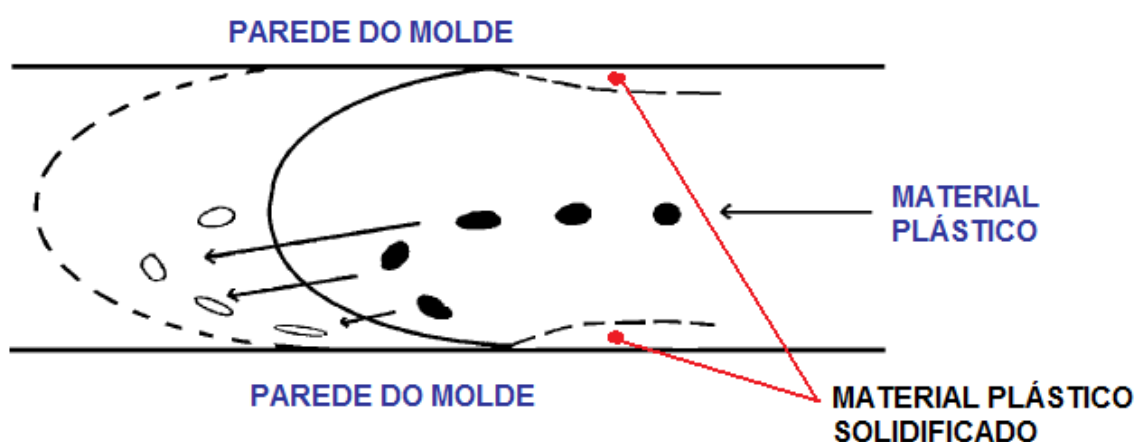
Escoamento do material fundido num canal de alimentação de um molde de injeção
